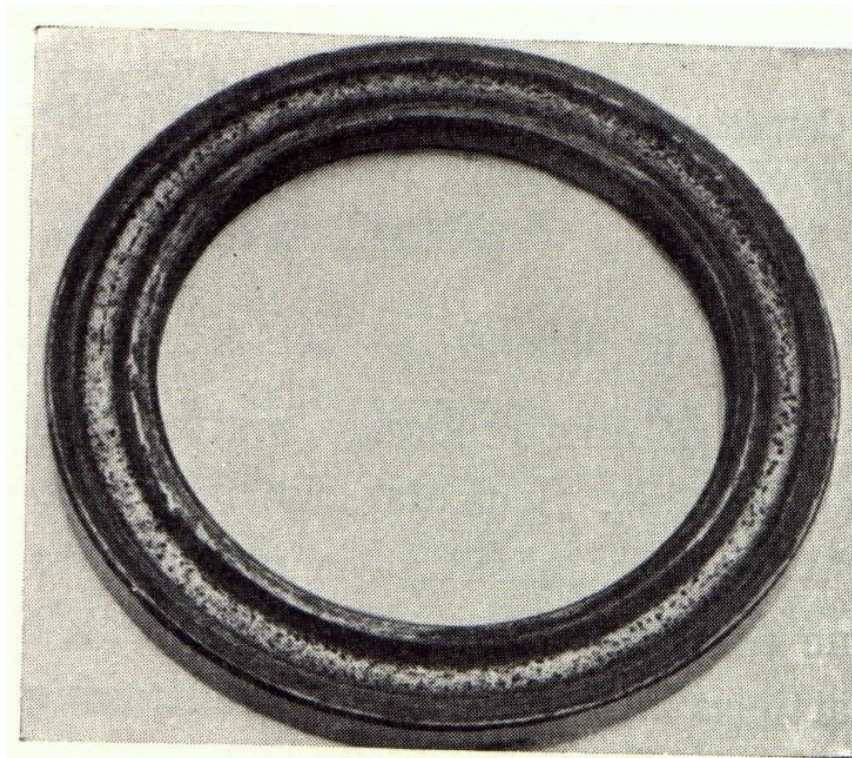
Aro de rodamiento axial corroído por la presencia de agua [2]
